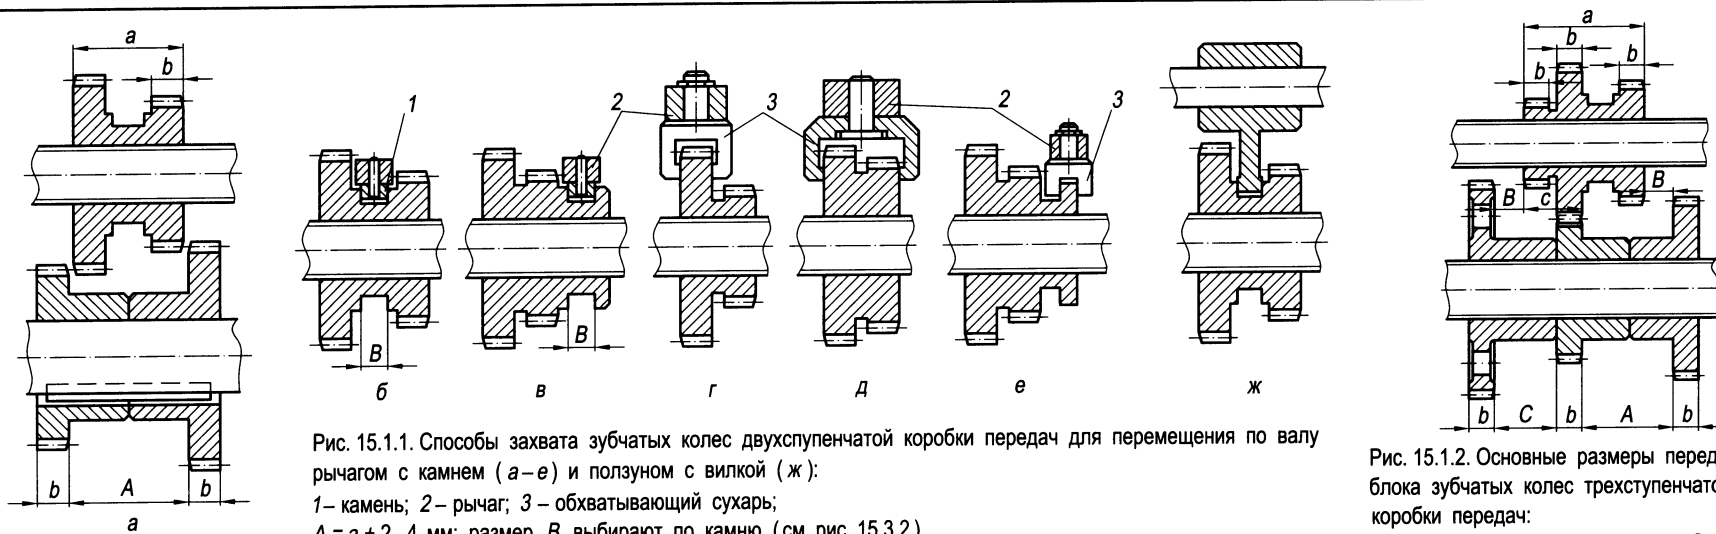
Способы захвата зубчатых колес двухступенчатой коробки передач для перемещения по валу рычагом с камнем (а–е) и ползуном с вилкой (ж):
